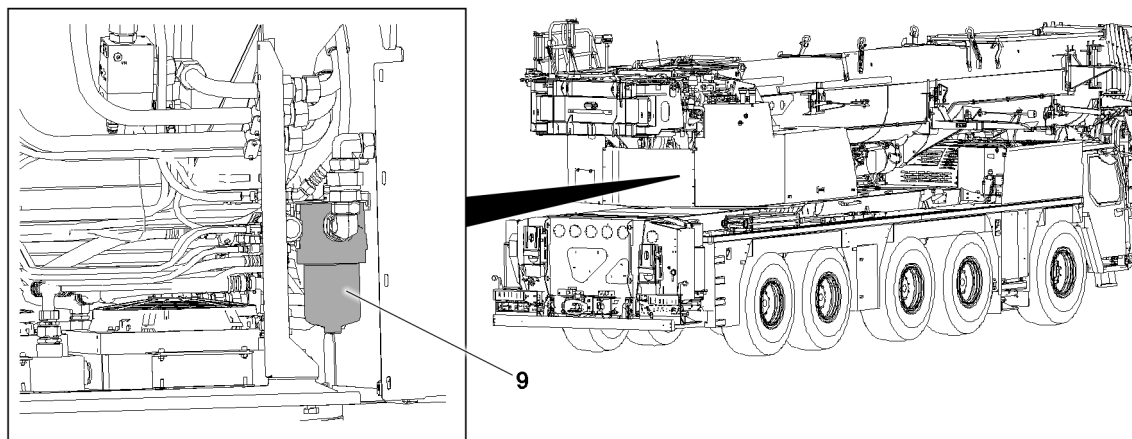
Filtro de tubulação com sensor eletrônico de manutenção
